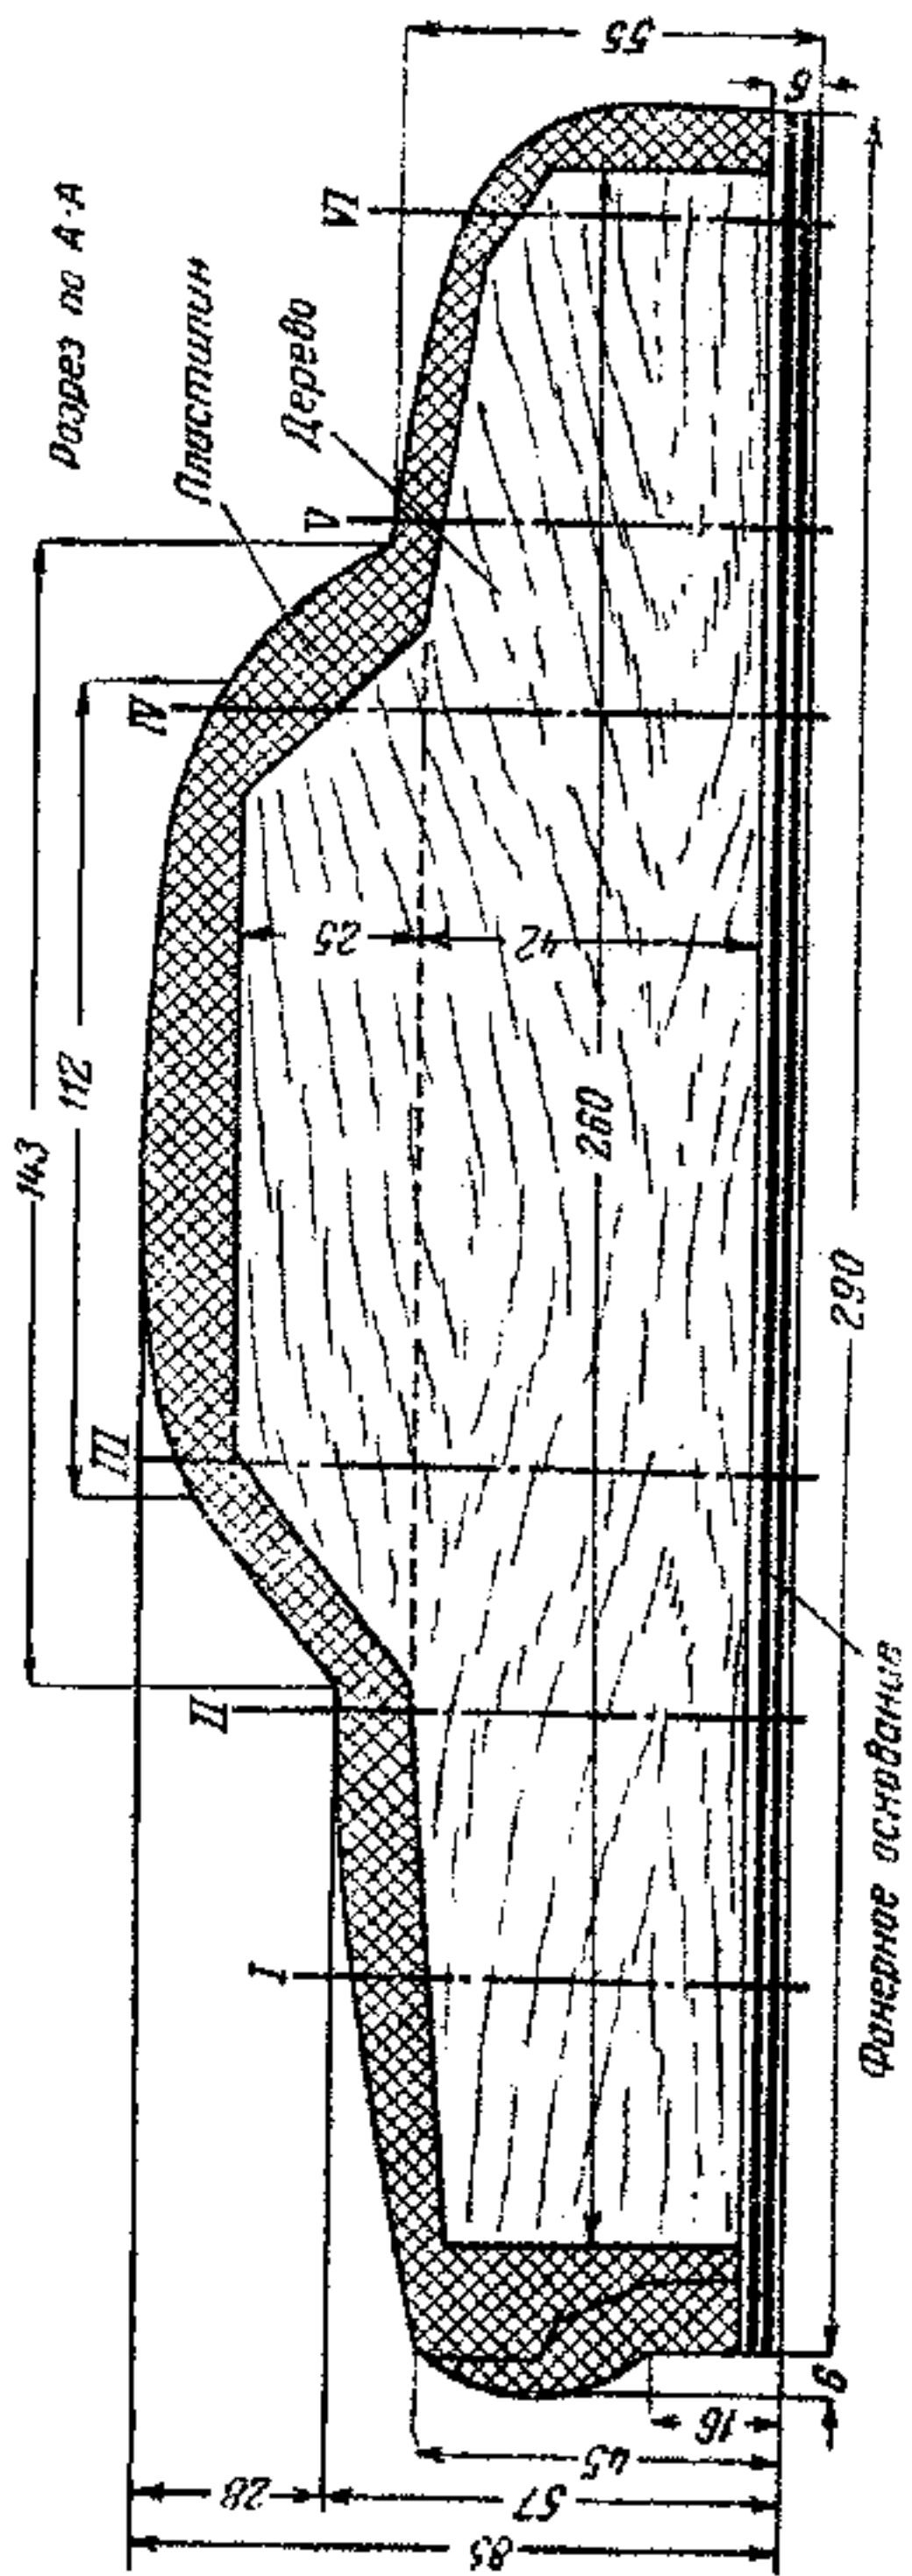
Болванка для выклейки кузова (вид сбоку)
